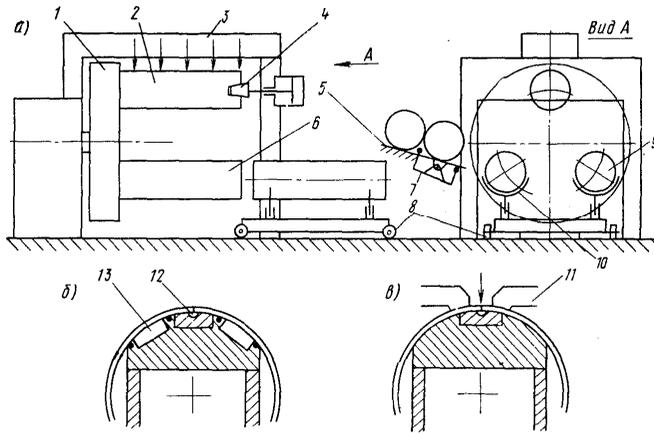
Полуавтоматическая установка для сборки и сварки продольного стыка обечайки:
